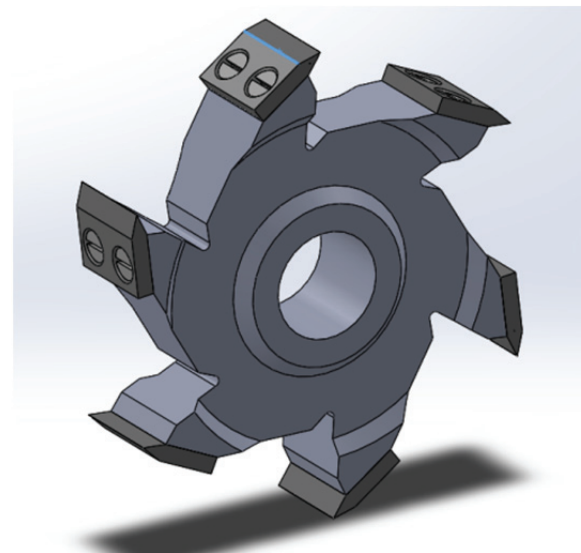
Трехмерная геометрическая твердотельная модель эффективной фрезы, сформированная в пакете Solid Works
